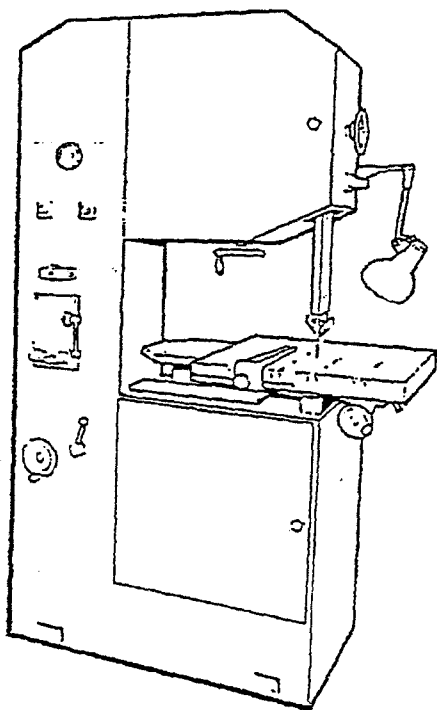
Вертикальний стрічковопиляльний верстат з нерухомою пиляльною рамою
